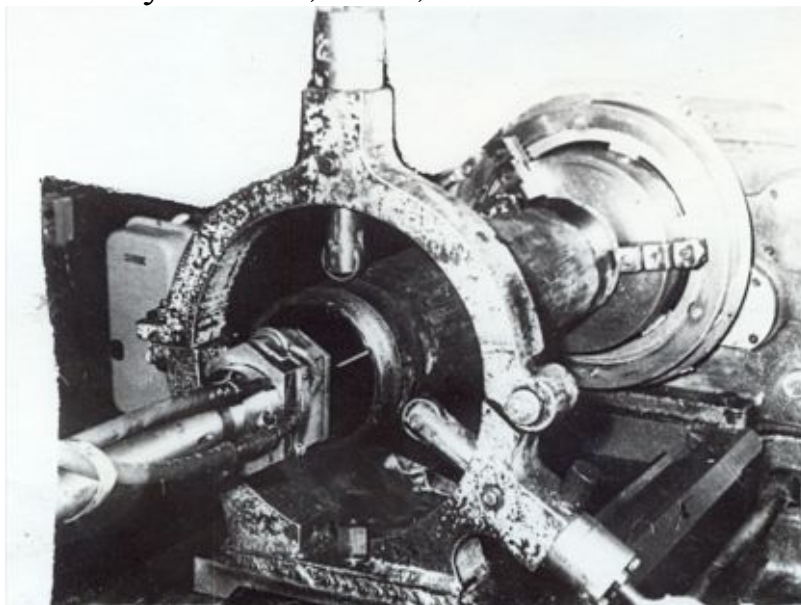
Опытная установка электромеханической обработки цилиндров (Рутченковский завод «Гормаш»)
